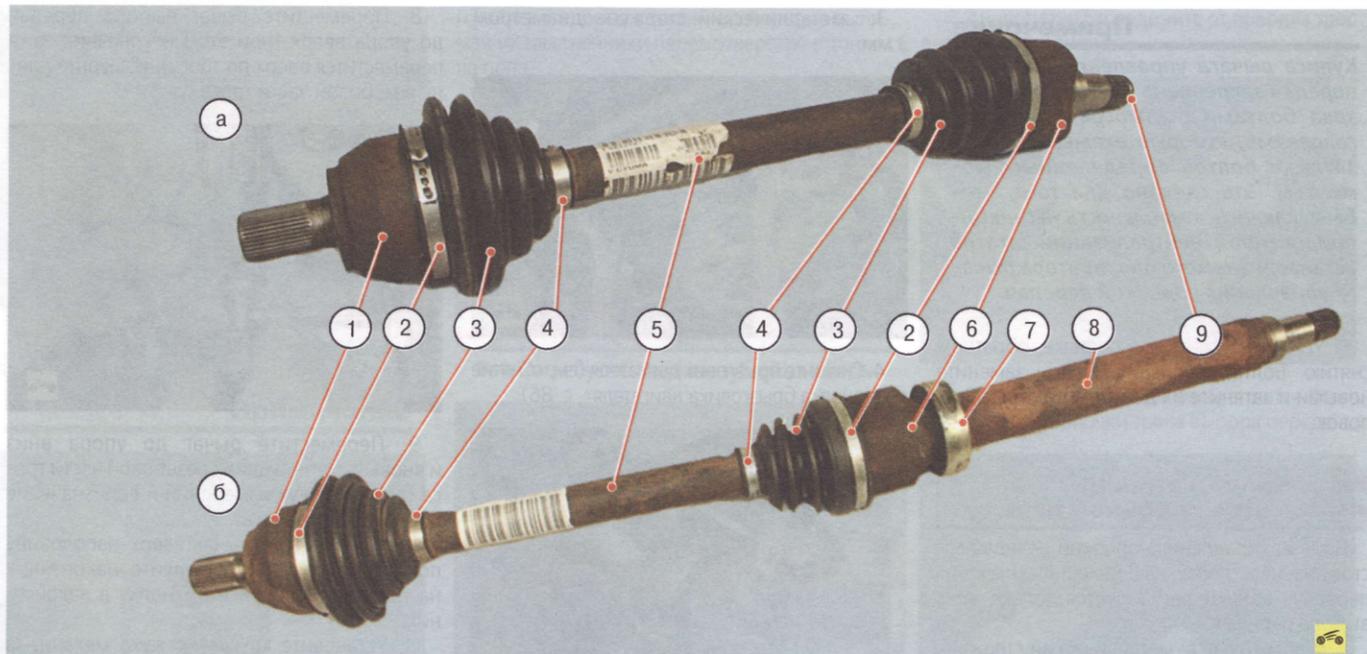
Приводы передних колес: а – привод левого переднего колеса; б – привод правого переднего колеса; 1 – наружные шарниры равных угловых скоростей; 2 – большие хомуты крепления чехлов шарниров; 3 – чехлы шарниров; 4 – малые хомуты крепления чехлов шарниров; 5 – валы приводов; 6 – внутренние шарниры равных угловых скоростей; 7 – подшипник промежуточной опоры; 8 – промежуточный вал; 9 – стопорное кольцо
